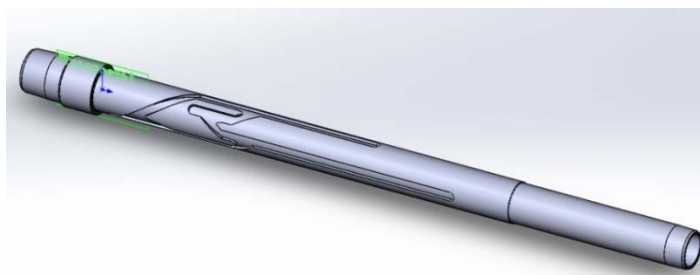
3D модель пакера 3 ПМС-118-52-70
